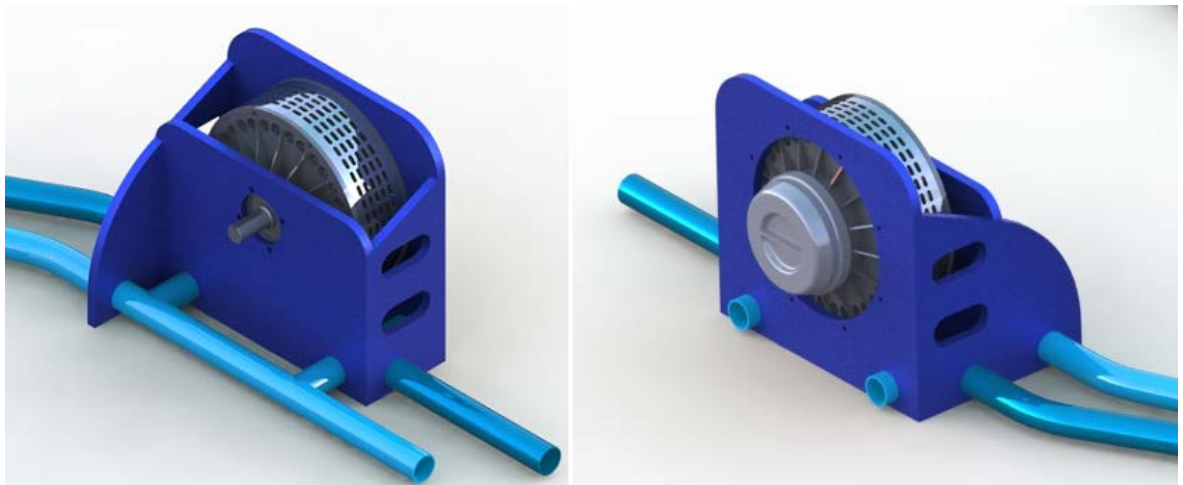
Vistas isométricas del soporte motor y del motor colocados en el chasis.
